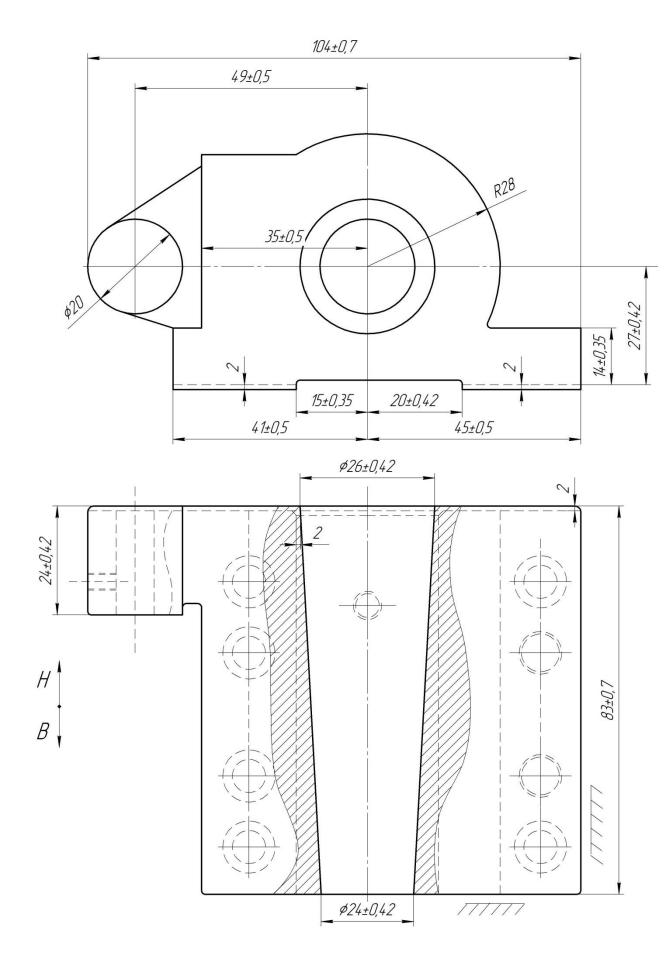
Общий вид заготовки - «Кронштейна»
